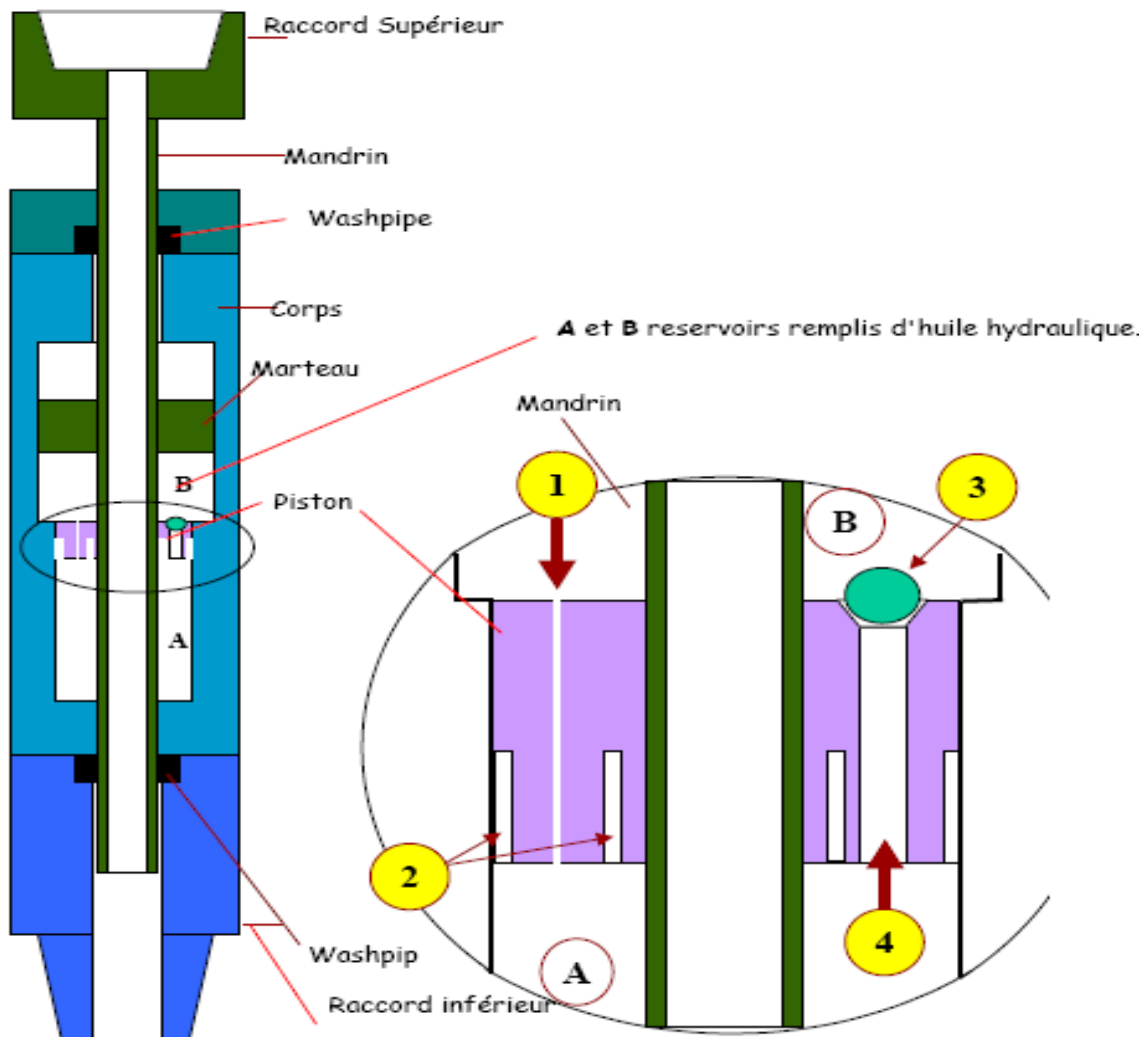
Schéma d'une coulisse hydraulique.^[8]
